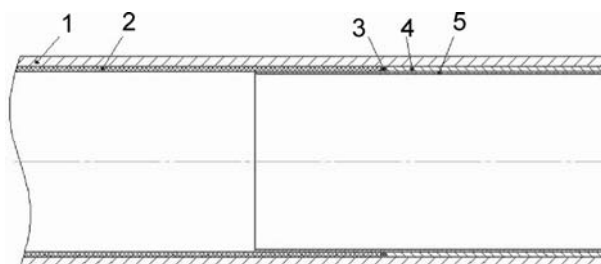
Стальная труба, футерованная полиэтиленовой трубой, подготовленная для соединения электродуговой сваркой:
